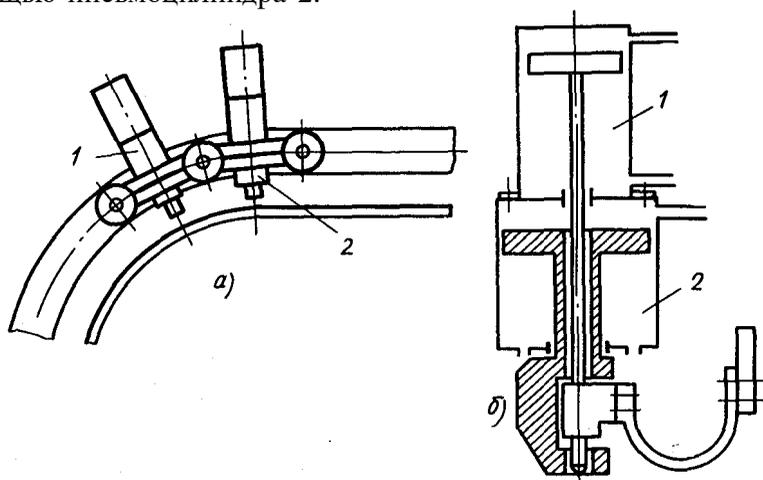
Схема двухточечной машины для сварки криволинейных швов
